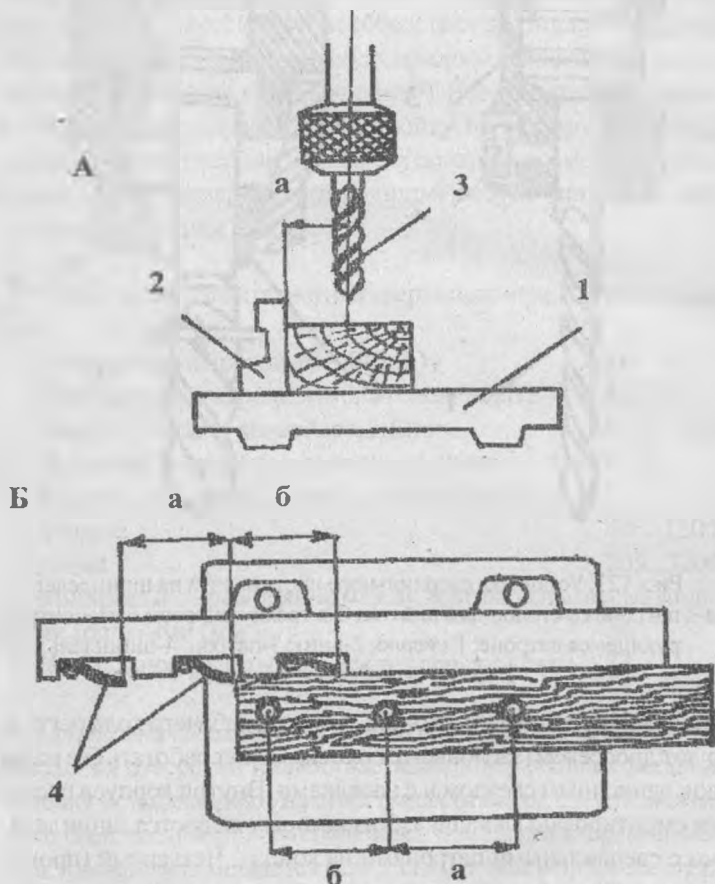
Настройка вертикального сверлильно-пазовального станка:
